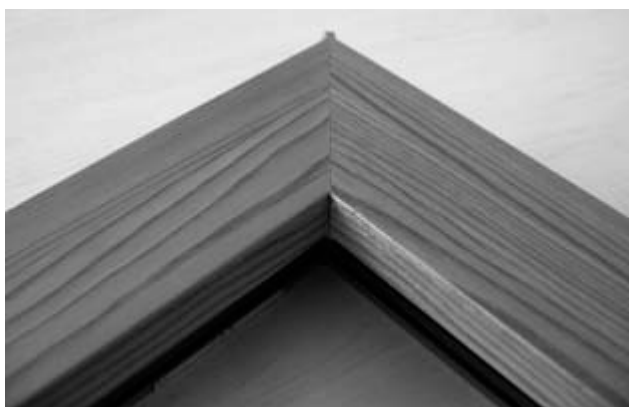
Вид сварного шва 0,2 mm
